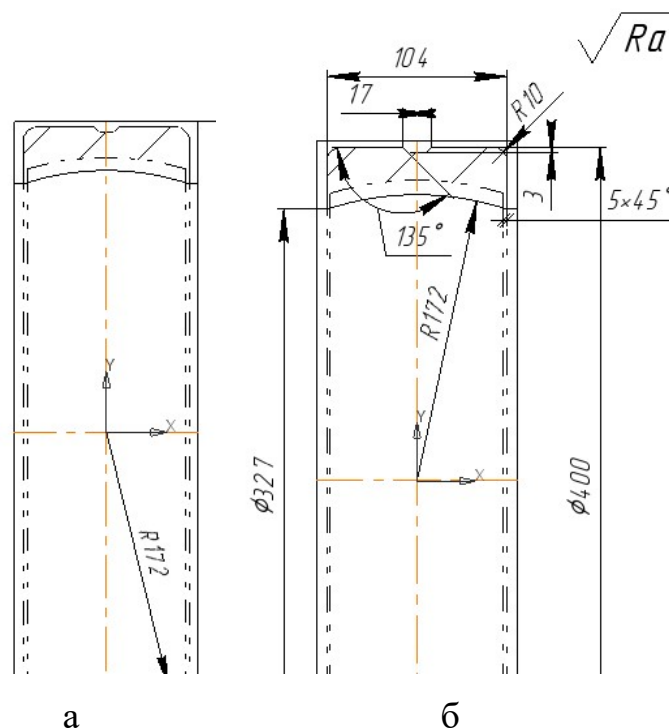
Креслення заготовки (а), креслення деталі (б) «Кільце підшипника»
